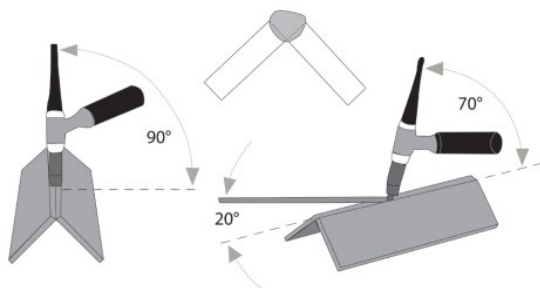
Положення «TIG-пальника» під час виконання зварювання кутового з'єднання.
